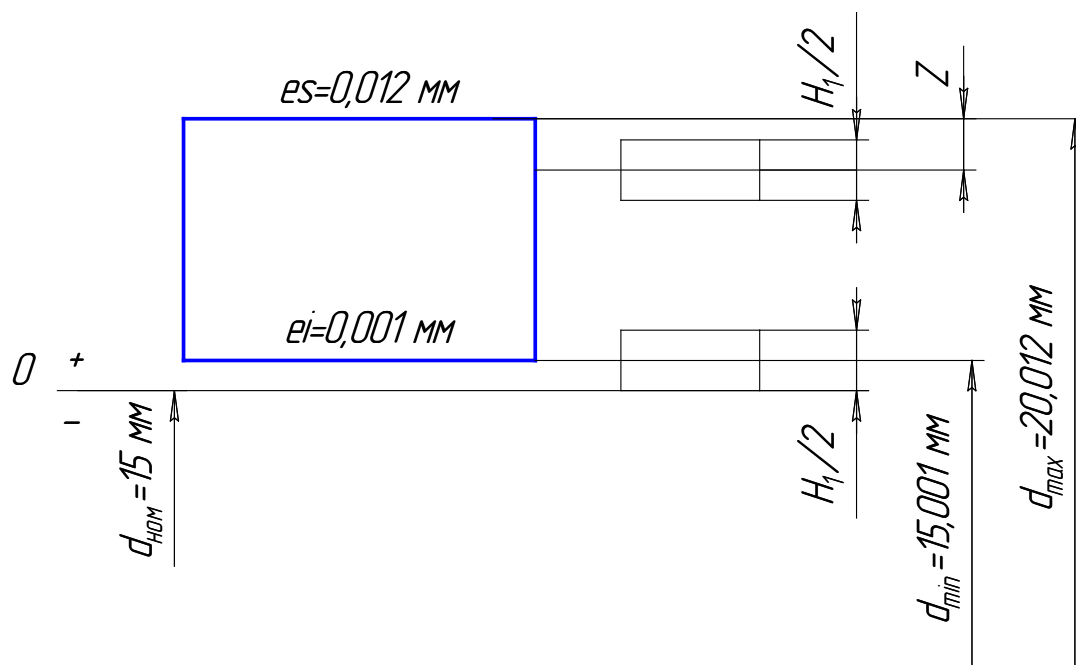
Схема розташування допусків робочих поверхонь скоби для контролю розміра $\varnothing 15k6^{+0,012}_{+0,001}$
